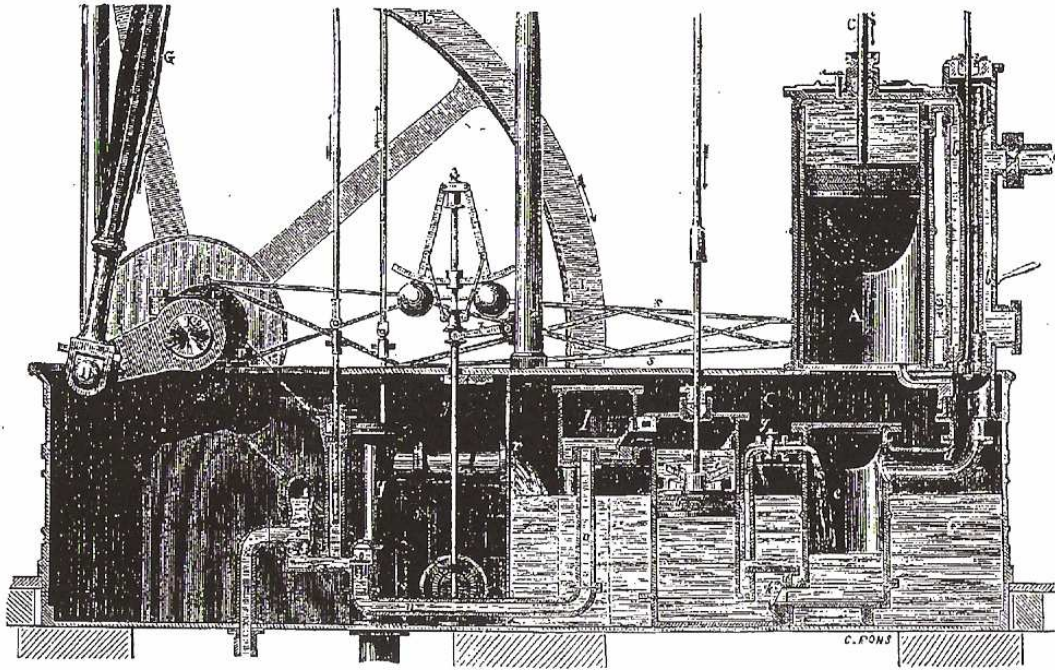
Coupe de la machine à condenseur, ou machine de Watt à basse pression.
